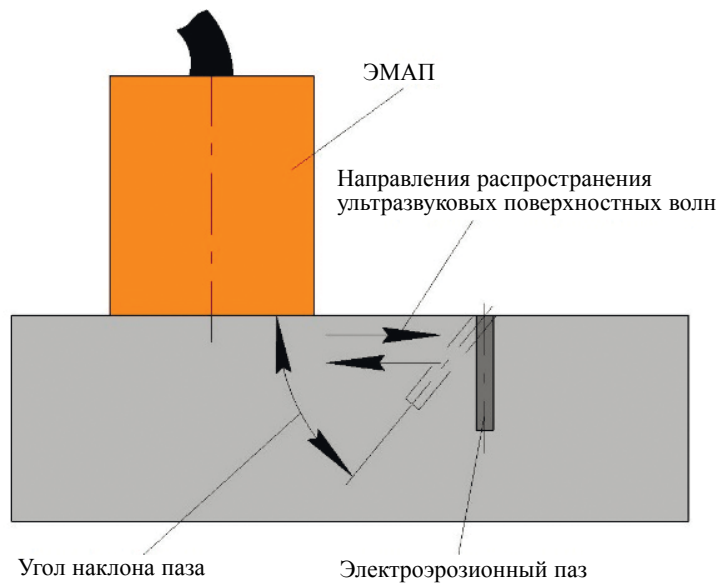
Схема измерения. Установка ЭМАП на образец.
